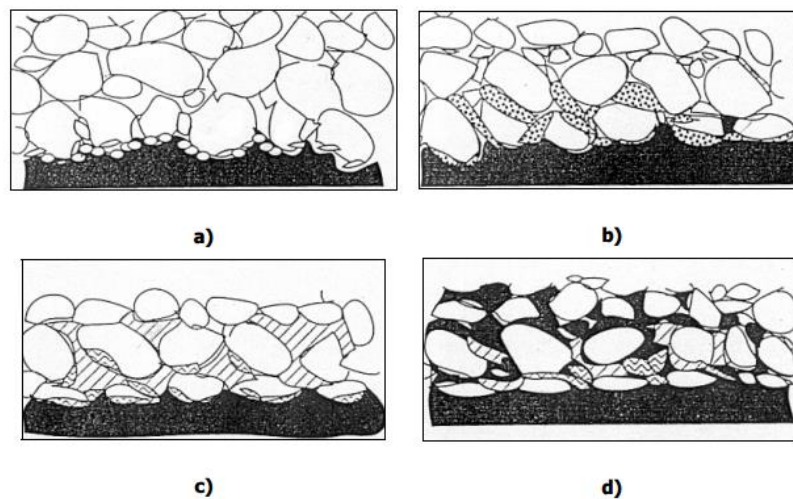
Defectos principales de penetración de metal en el molde a) Superficie rugosa, b) Burn-on, c) Burn-in y d) Penetración de metal (J Z. Janjusevic et al., "A Contribution to Study of Processes on the Steel CastSand Mould Contact Surface during Casting, *Materials Letters* 45, 2000, pp. 234-235.)
